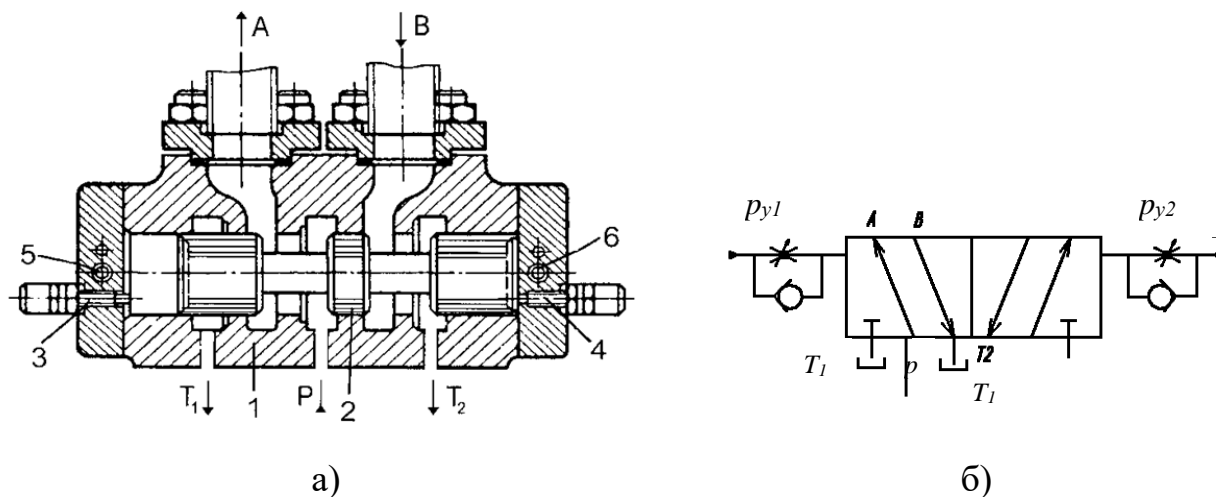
Золотниковый распределитель с гидроуправлением:
